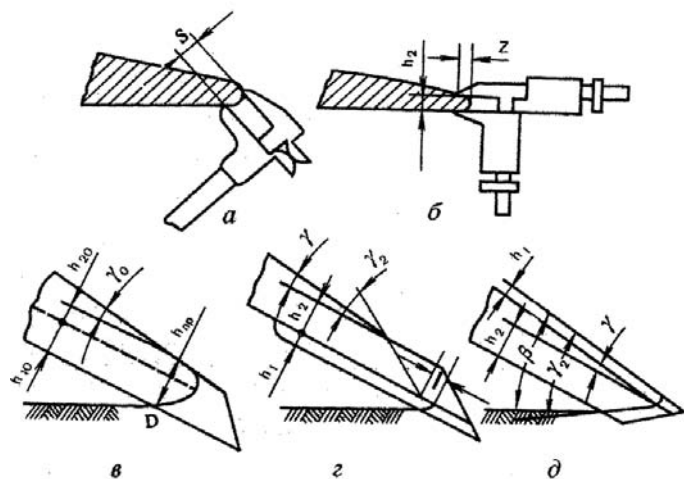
Схемы лезвий почворезущих деталей и методов их контроля: а – контроль ширины затылочной фаски S ; б – контроль толщины h_z режущей кромки на расстоянии Z от вершины; в – однородное затупляющееся лезвие; г, д – самозатачивающиеся лезвия с нижним и верхним расположением режущего (наплавленного) слоя; γ_1 – угол клина однородного лезвия; $h_{пр}$ – предельная толщина однородного лезвия; h_{10} – условная толщина нижнего слоя однородного лезвия; h_{20} – условная толщина верхнего слоя однородного лезвия; h_1 – толщина режущего слоя самозатачивающегося лезвия; h_2 – толщина несущего слоя самозатачивающегося лезвия; γ – угол клина самозатачивающегося лезвия; γ_2 – угол самозатачивания; β – угол крошения
